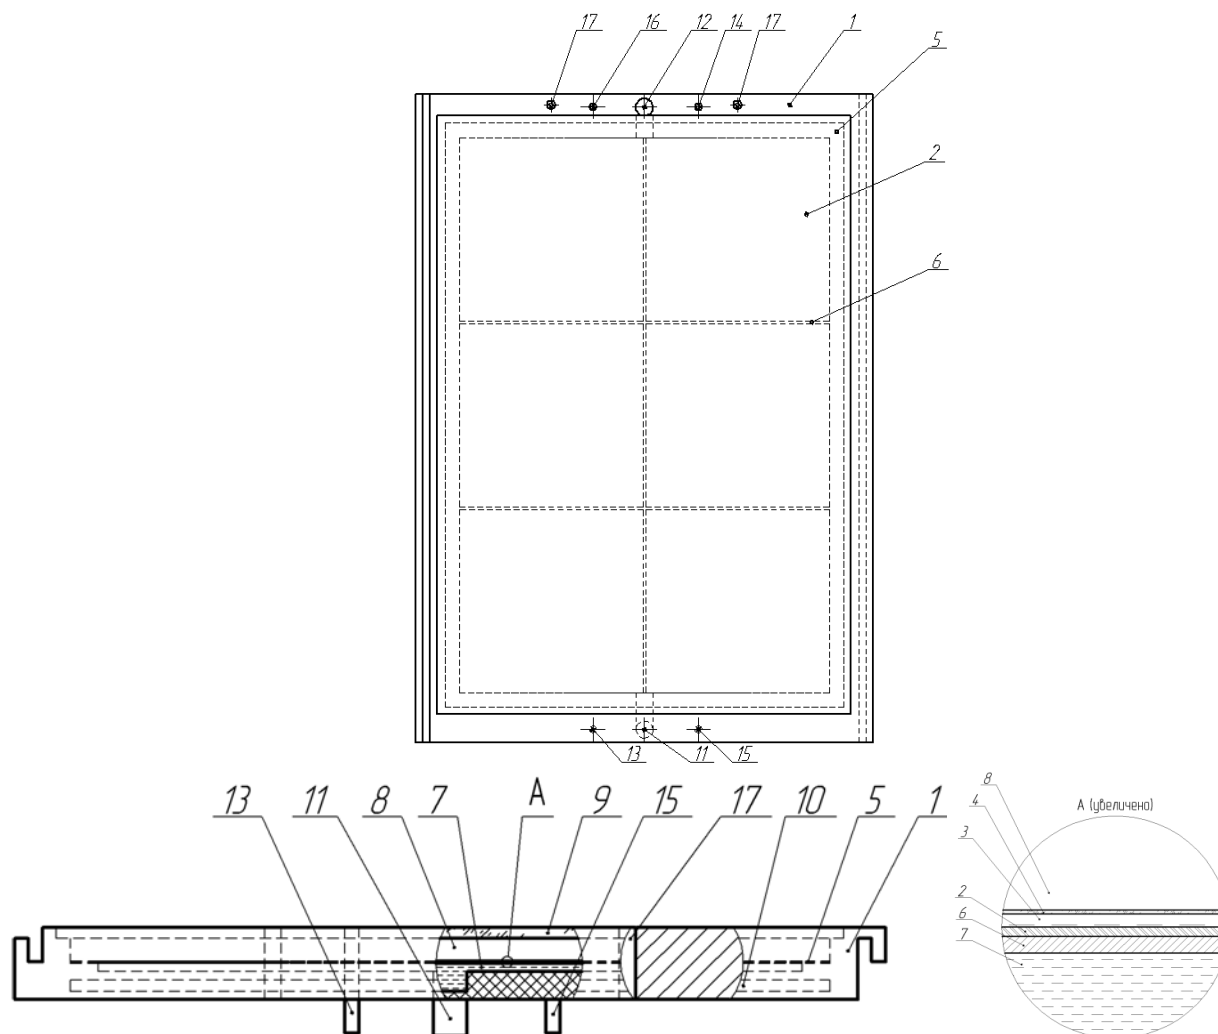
Планарная теплофотовольтовая кровельная панель: сверху – вид сверху, снизу – вид спереди и выносной элемент
